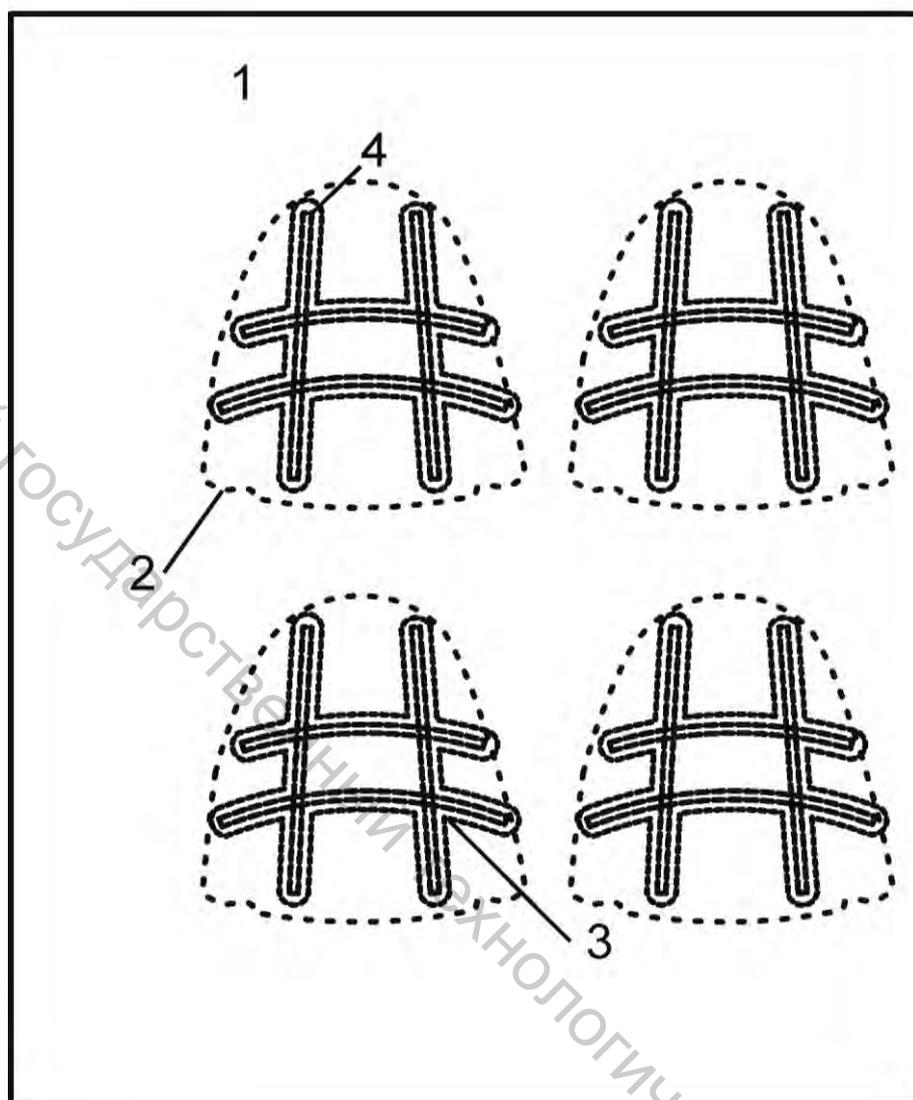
Пластина кассеты швейного полуавтомата:
